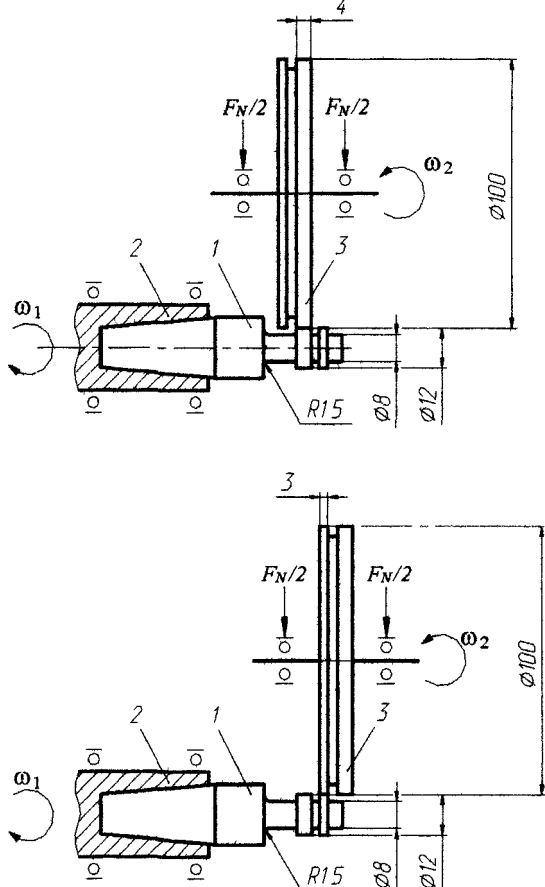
Модель зубчатых зацеплений для шестерен № 4 и № 11 коробки передач ПК.
